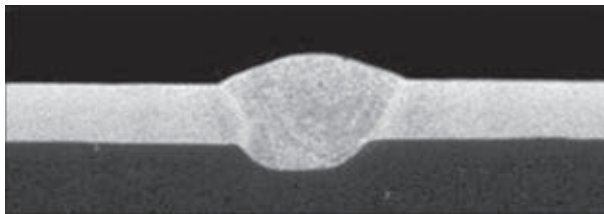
Макрошлиф сварного соединения из сплава Д16 толщиной 2 мм, сваренного плазменно-дуговой сваркой в нижнем положении
